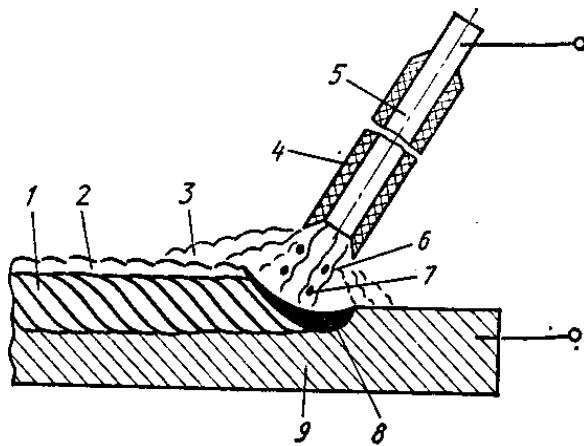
Схема ручного дугового зварювання металевим покритим електродом: 1– шов; 2 – шлак; 3 – захисна газова атмосфера; 4 – електродне покриття; 5 – електрод; 6 – електрична дуга; 7 – краплі електродного металу; 8 – зварювальна ванна; 9 – заготовка
